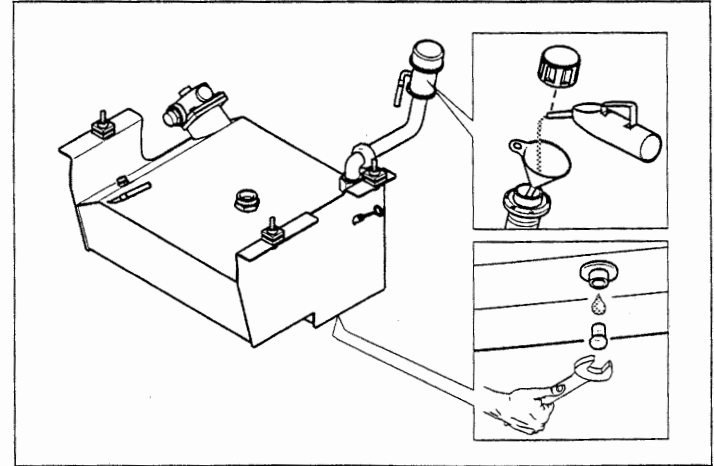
Ölablaßschraube am Hydraulikölbehälter
